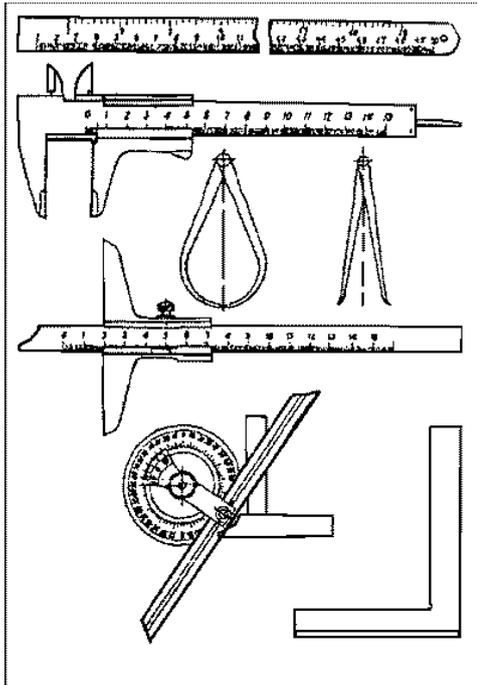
Универсальные измерительные инструменты: а – мерная металлическая линейка; б – штангенциркуль; в – кронциркуль нормальный; г – нутромер нормальный д – штангенглубиномер; е – угломер универсальный; ж – угольник плоский на 90°
